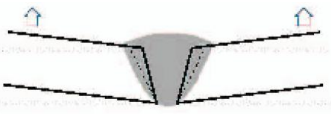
PRESENTACIÓN DE GRIETAS EN JUNTAS SOLDADAS
